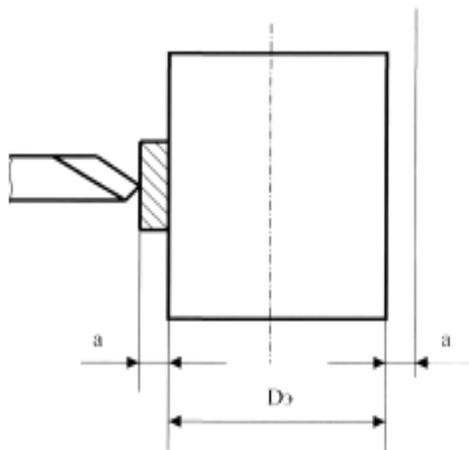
Схема настройки режущего инструмента на размер по щупу
